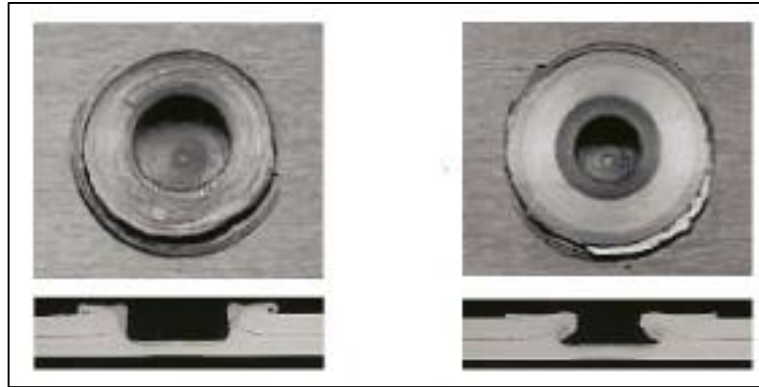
état de surface d'une soudure FSSW (37)
